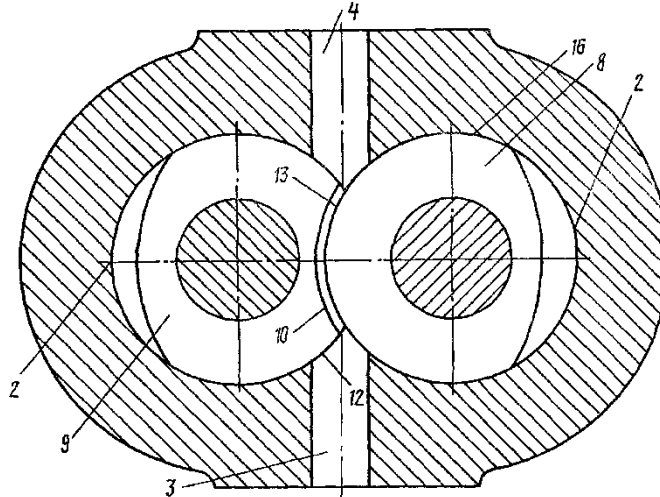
Схема розташування розвантажувальних каналів на поверхні дугоподібної виїмки [67]: 1 – корпус насоса; 2 – циліндричні розточки корпусу; 3 – порожнина високого тиску; 4 – порожнина низького тиску; 8 і 9 – підшипники ковзання; 10 – поверхня з'єднання підшипників по дугоподібній виїмці 11 з циліндричною поверхнею 16; 13 – розвантажувальні канали.
